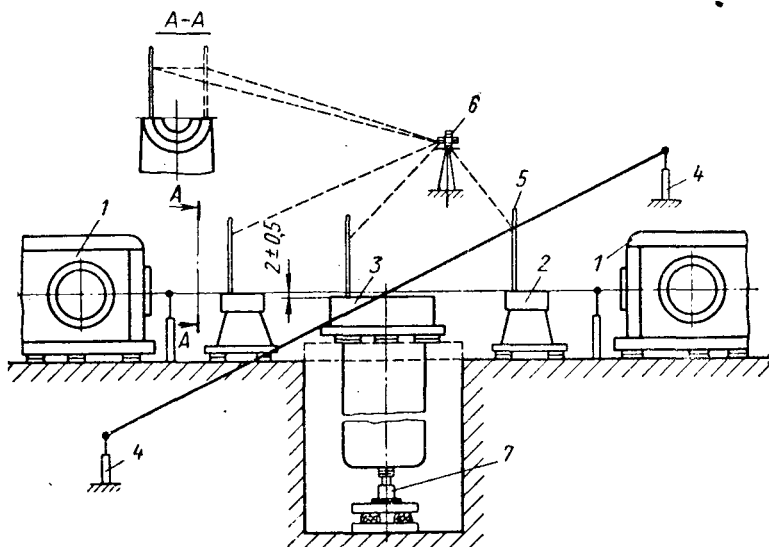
Схема монтажа электродвигателя двухкорпусного оппозитного компрессора:
